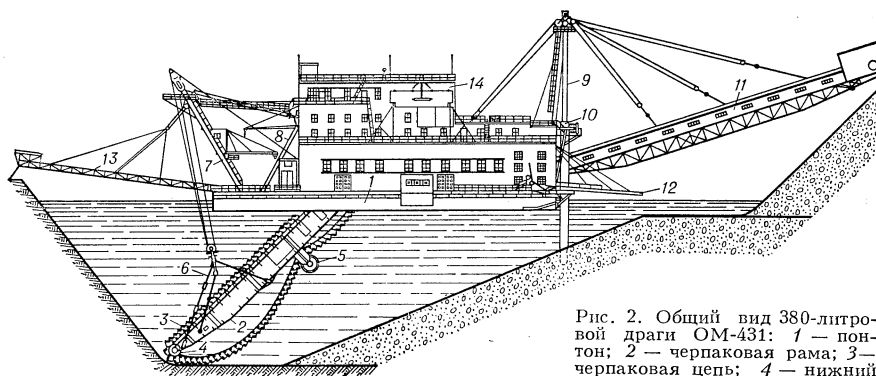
Общий вид 380-литровой драги ОМ-431: 1 — понтон; 2 — черпаковая рама; 3 — черпаковая цепь; 4 — нижний черпаковый барабан; 5 — подвес черпаковой рамы; 6 — передняя мачта; 7 — задняя мачта; 8 — главная ферма (суперструктура); 9 — задняя мачта; 10 — сваи; 11 — отвалообразователь (стакер); 12 — хвостовые колоды; 13 — береговой мостик; 14 — надстройка.
